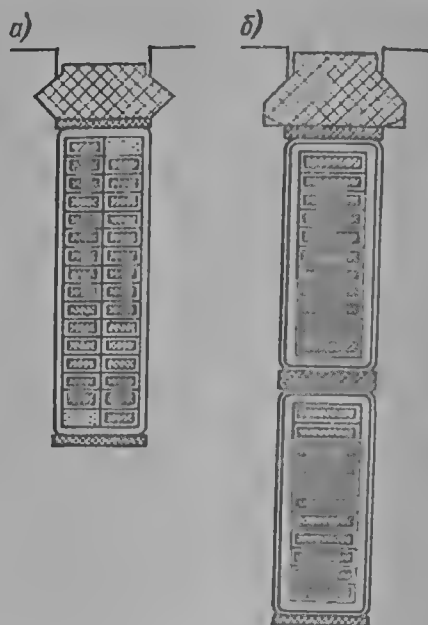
Сечение паза статорной обмотки: а — однослойной; б — двухслойной
